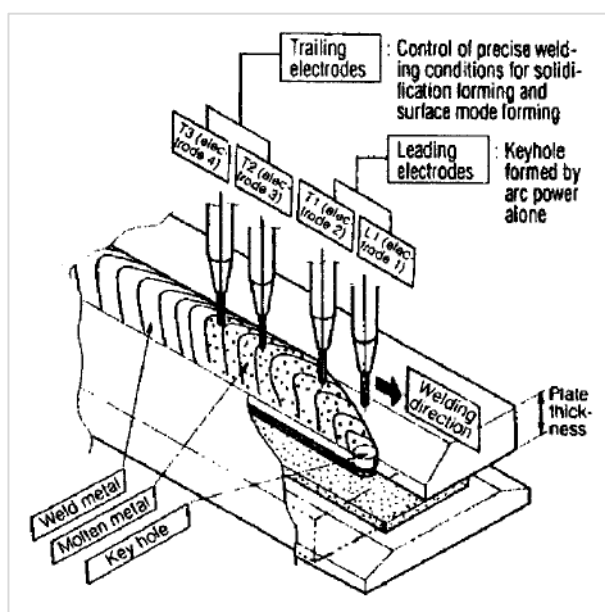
Ilustração do processo de soldadura *NH-HISAW* [13]
